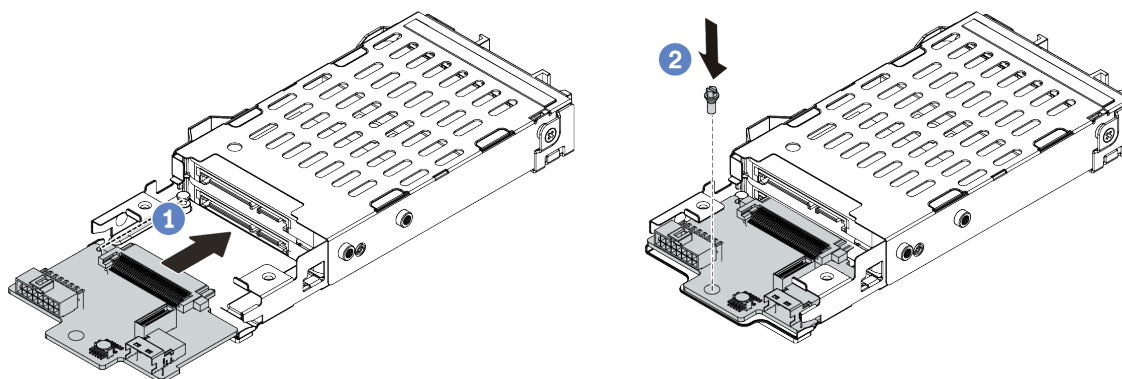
Installation du fond de panier d'unité 7 mm (bas)
